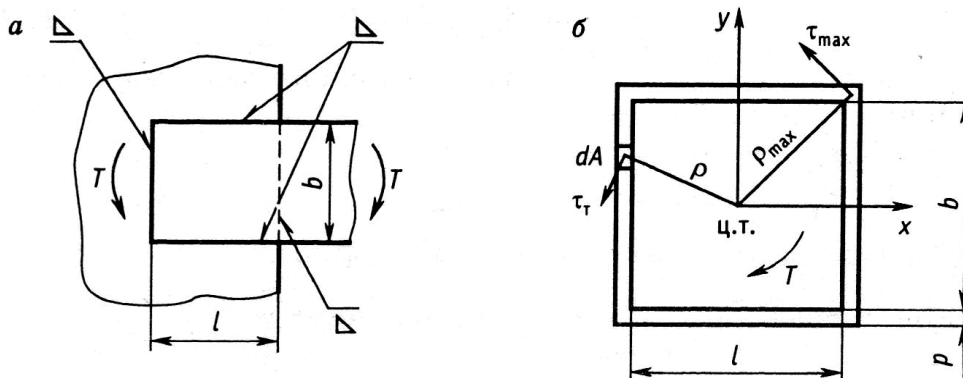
Расчетные схемы нахлесточных сварных соединений, нагруженных в плоскости стыка моментом  $T$ : а – схема нагружения; б – опасное сечение шва
